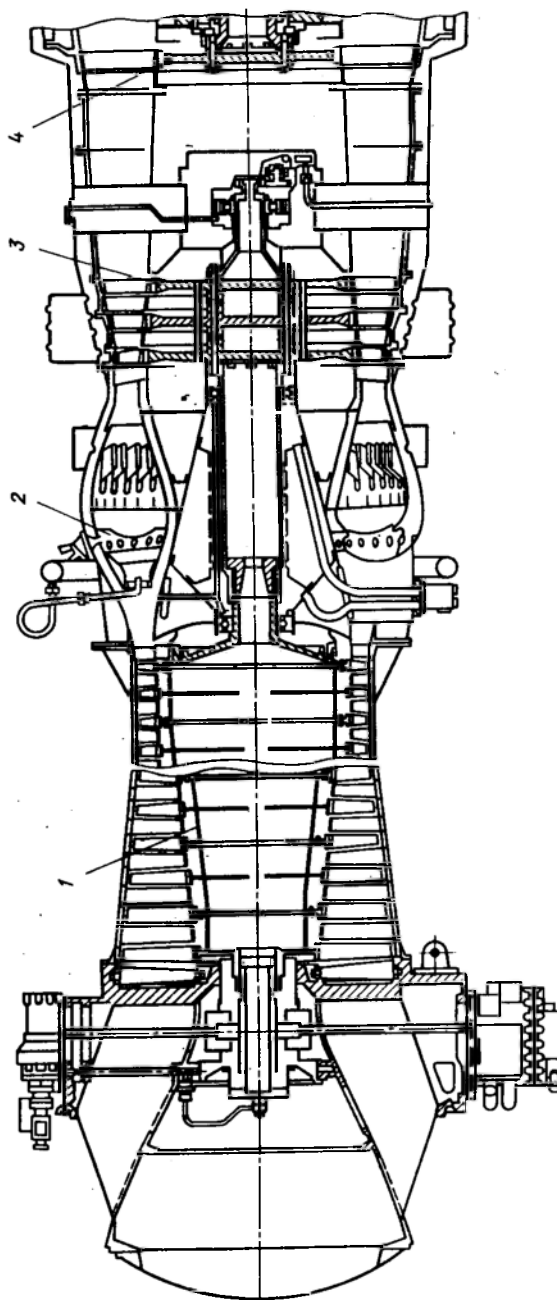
Продольный разрез двигателя НК-12СТ
